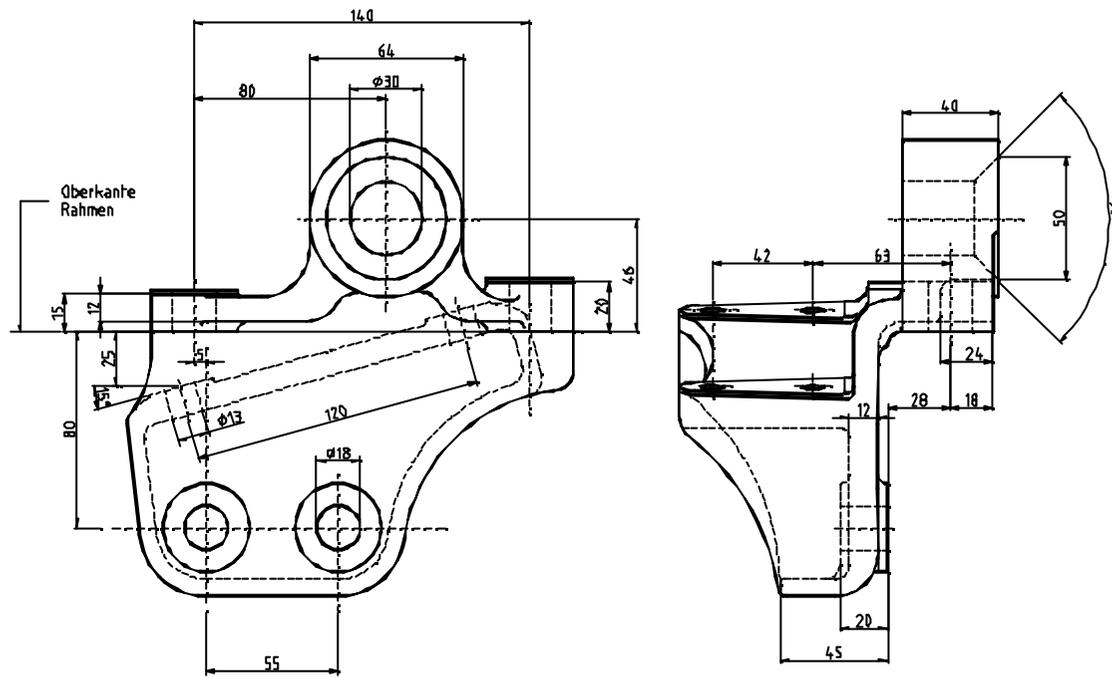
Frontanbaubock BM 437 (linke Ausführung) MB-Nr. A 425 552 06 18
